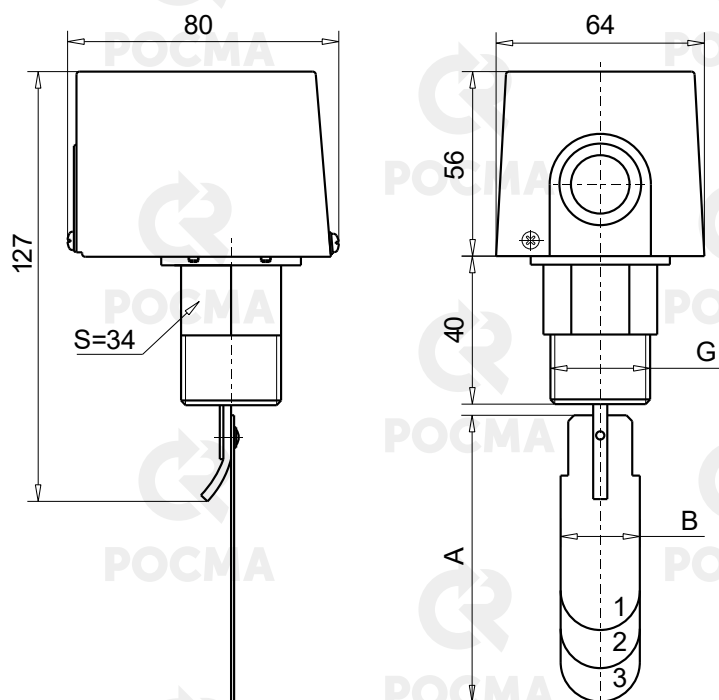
Габаритные и присоединительные размеры моделей РП-1 и РП-2.
